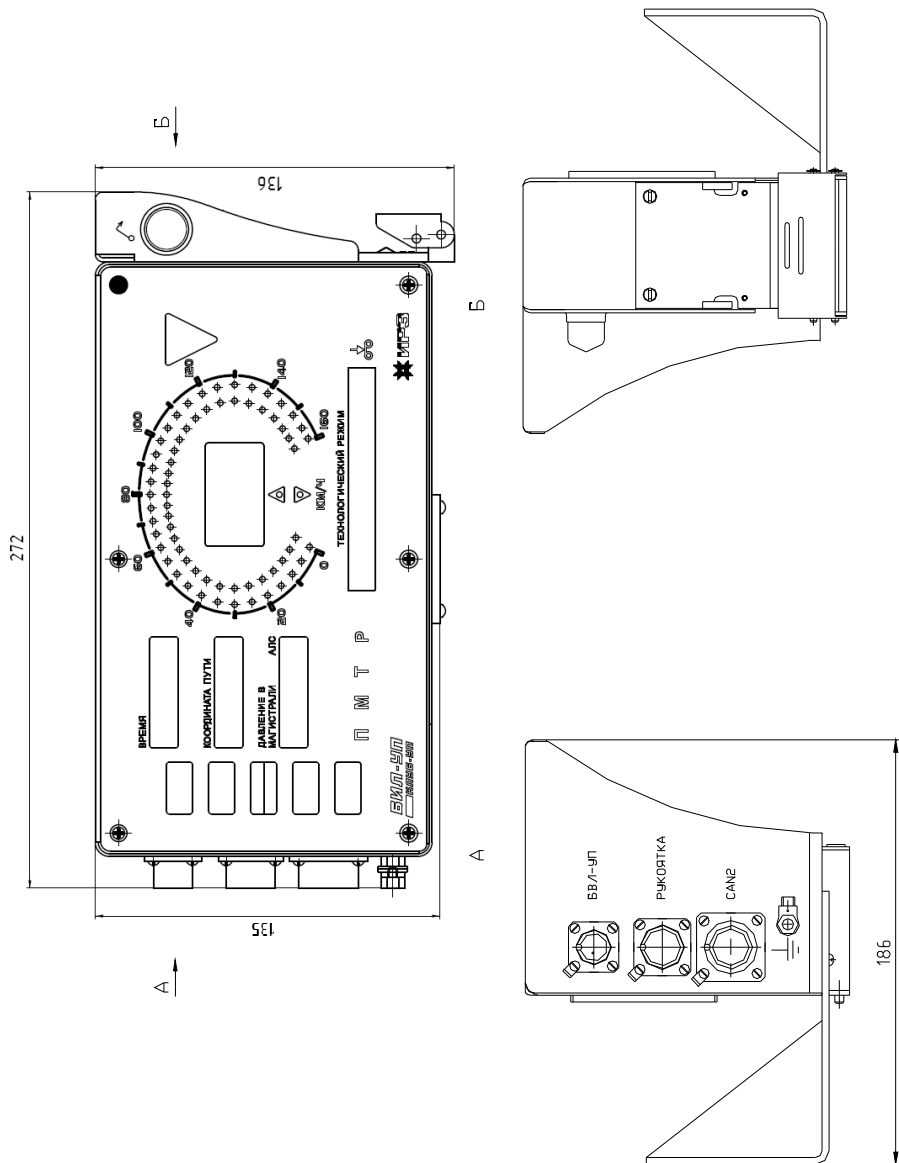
Внешний вид и габаритные размеры блока БИЛ-УП 36993-310-00
